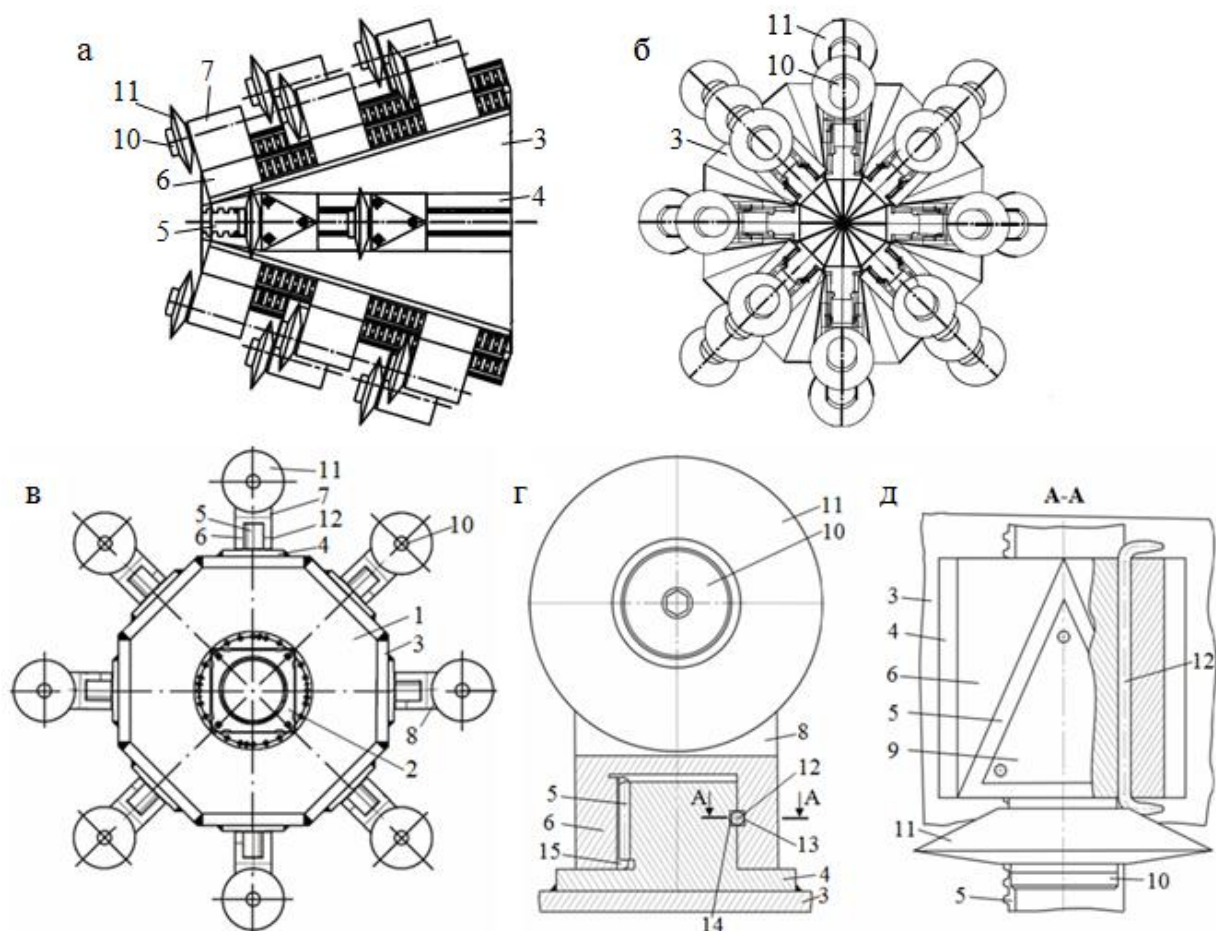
Радиальная корона с дисковым инструментом на корпусе-пирамиде: а – общий вид; б – вид спереди; в – вид на большее основание; г – зубчато-реечный замок трехгранной призмы; д – зона размещения проволочного фиксатора
